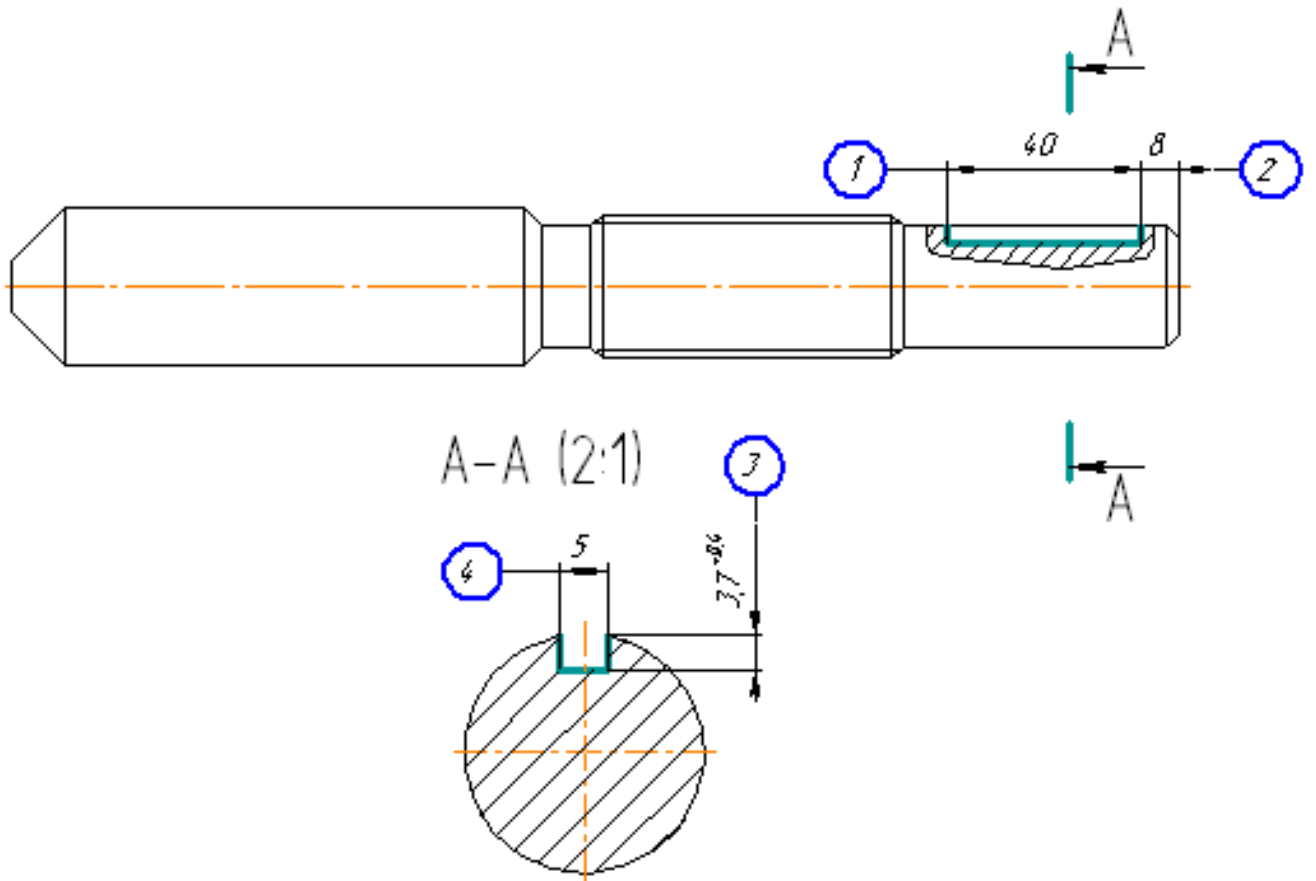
Ескіз обробки заготовки на операції 015
